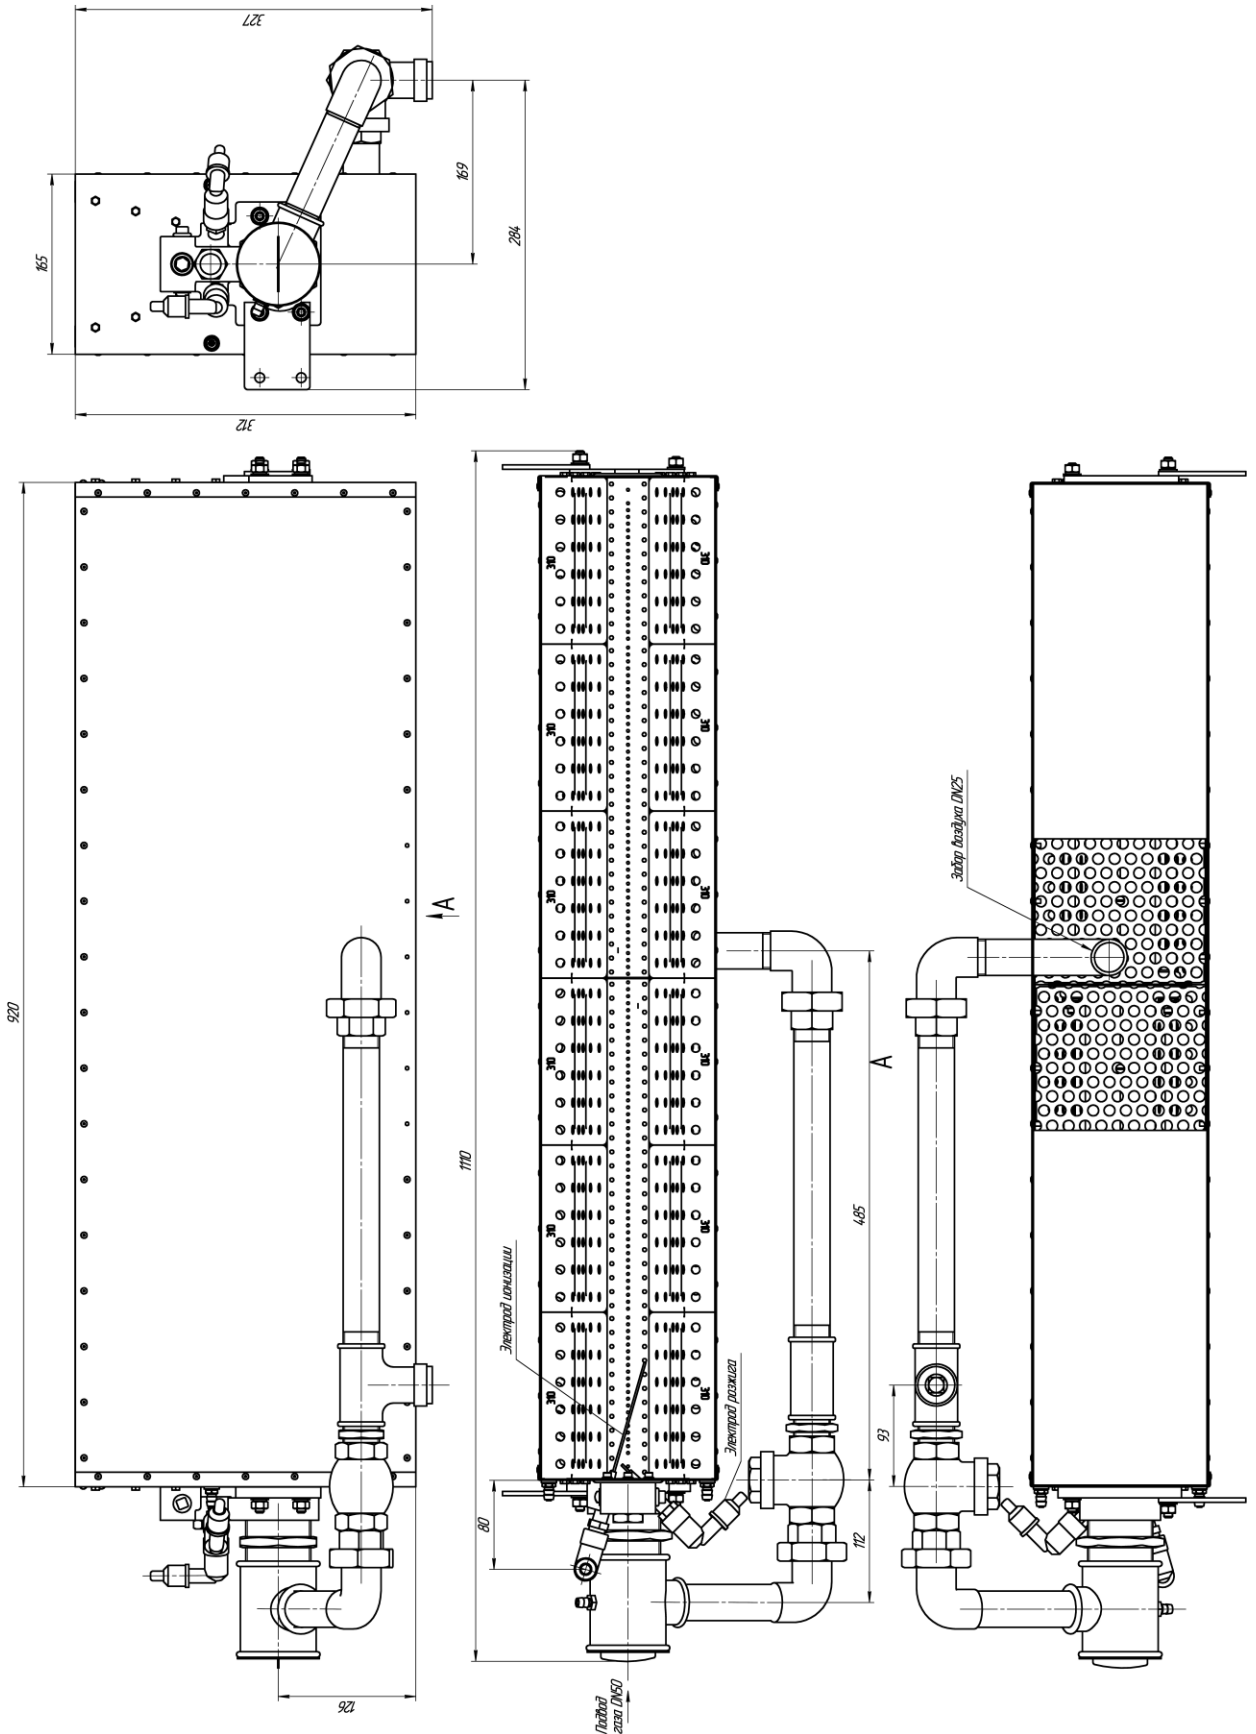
Чертеж общего вида горелки ГТТ700
